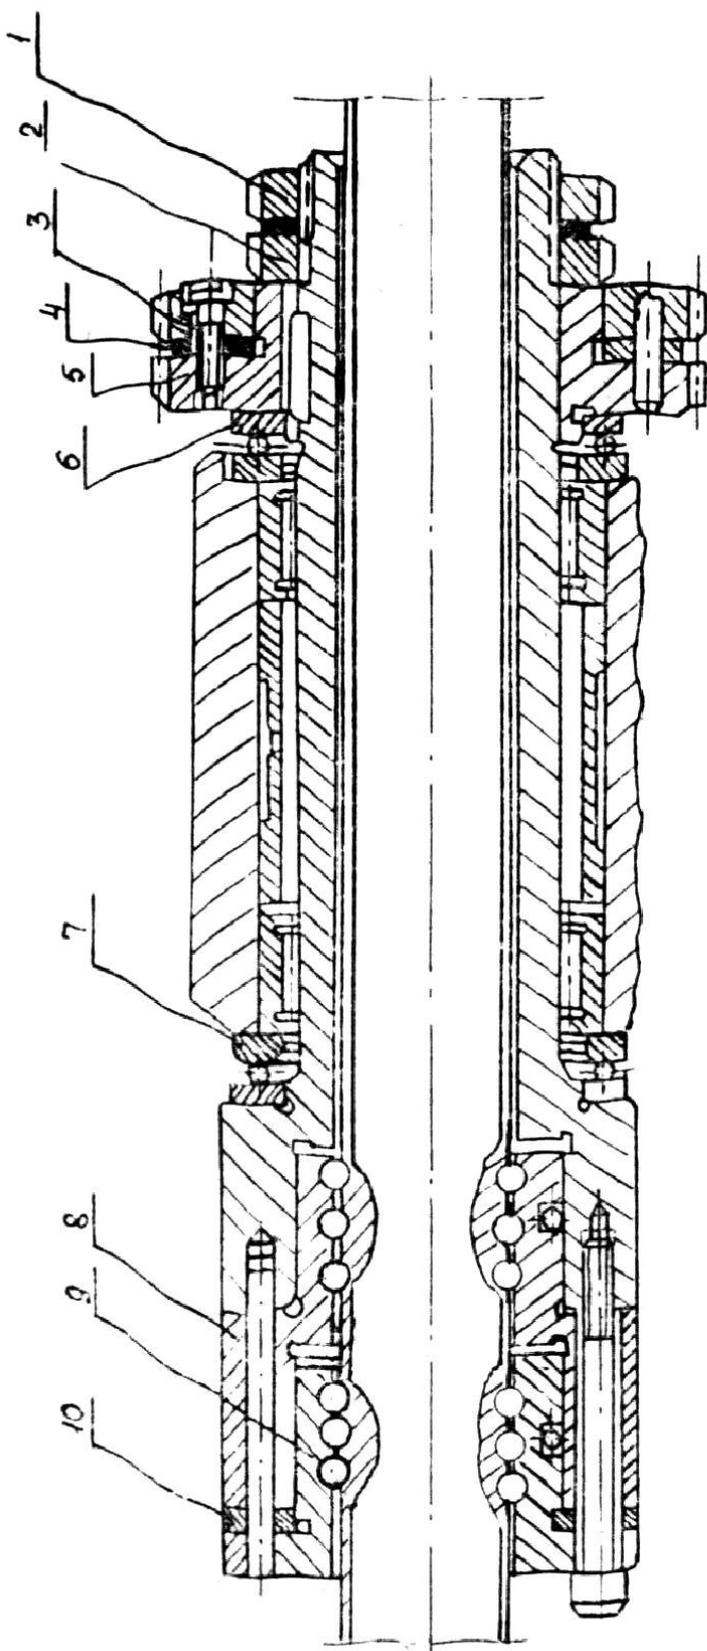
Шариковая винтовая пара привода механизма подачи стола и салазок
